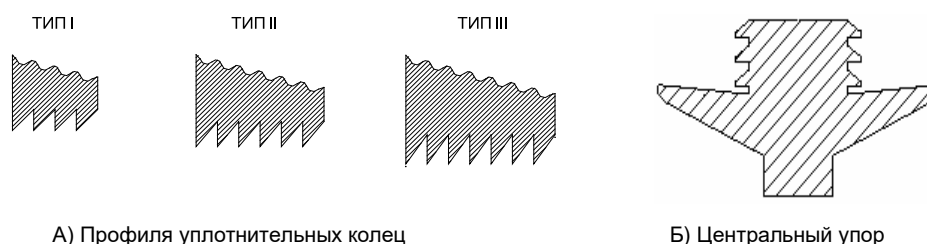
Внешний вид профилей уплотнительных колец и центрального упора
